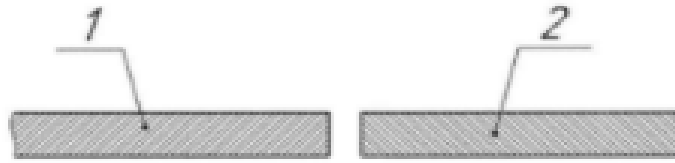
Конструкція зварного з'єднання без оброблення крайок
